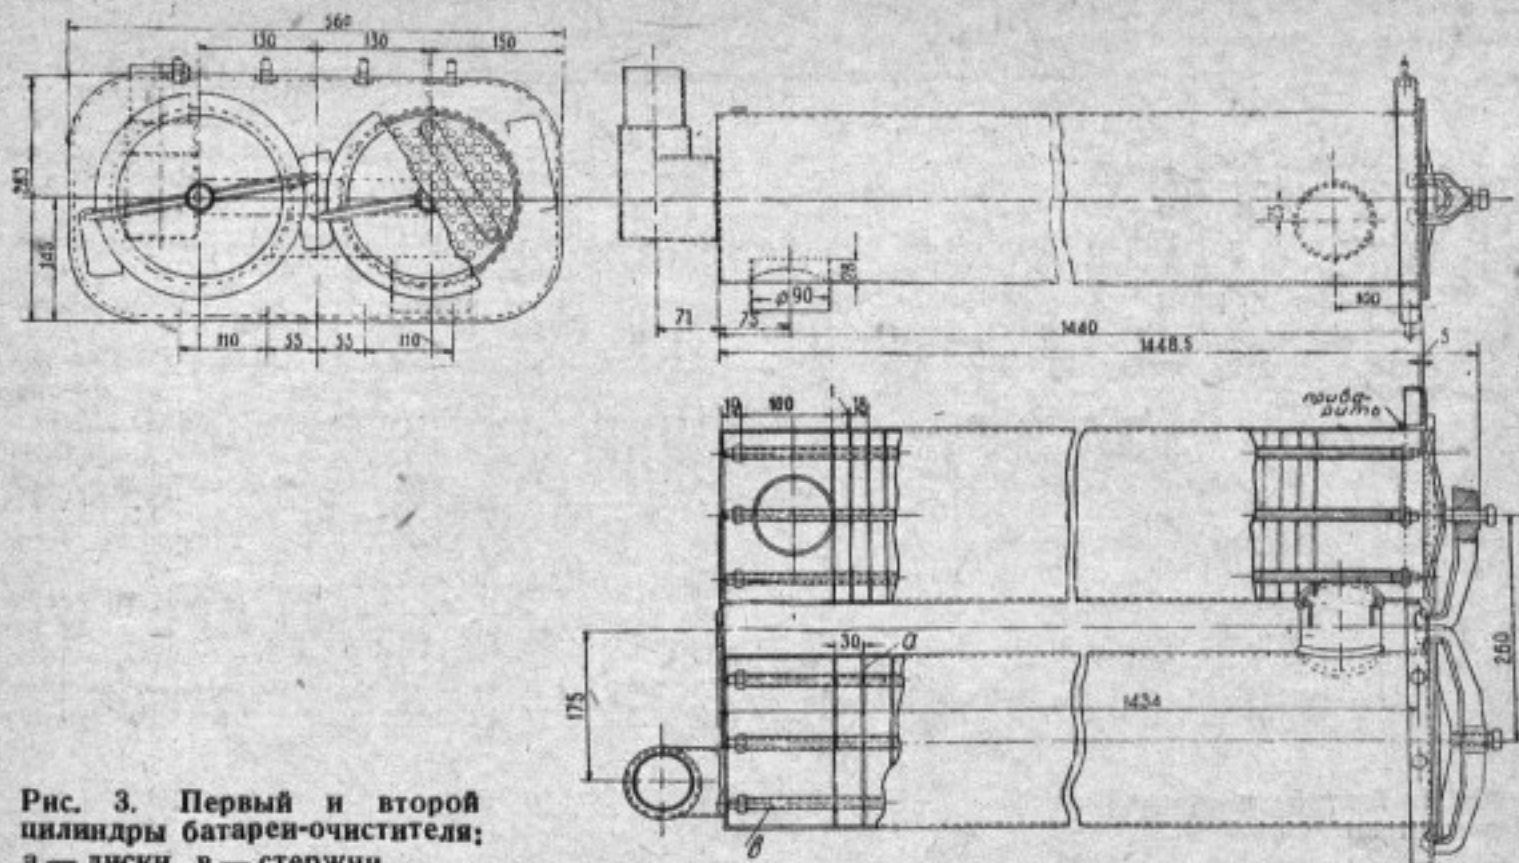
Первый и второй цилиндры батарей-очистителя; а — диски, в — стержни
